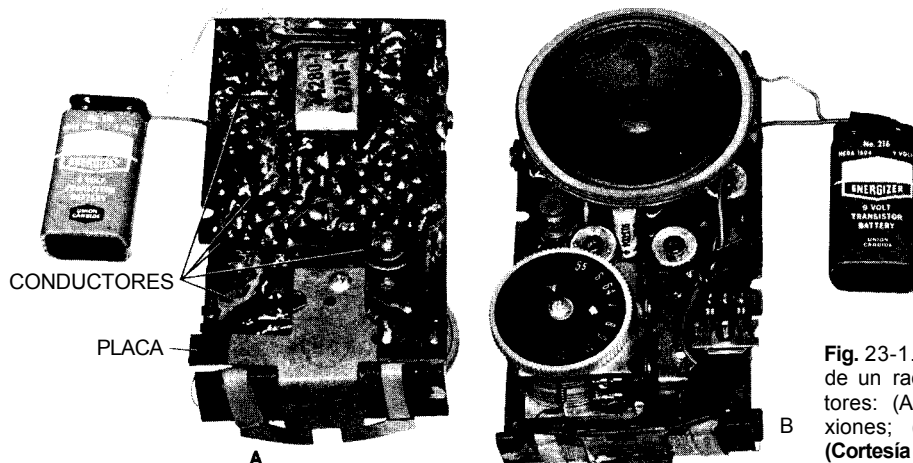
Conjunto del circuito impreso de un radioreceptor pequeño de transistores: (A) conductores o cara de conexiones; (B) lado de los componentes (Cortesía de Maxwell).
